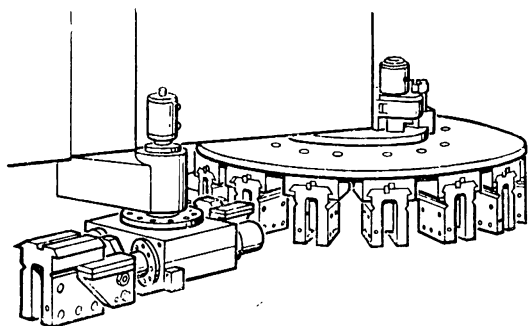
Магазин и двух-захватный автооператор для автоматической смены инструментодержателей станков фирмы DÖRRIES
